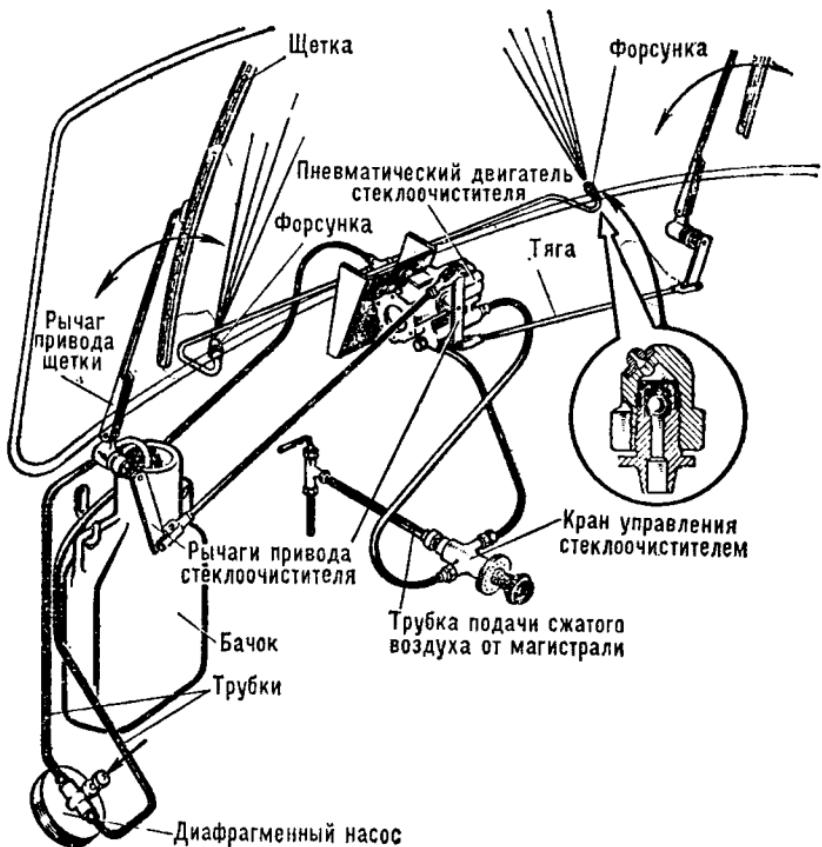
Устройство для очистки и обмыва ветрового стекла автомобиля ЗИЛ-130
